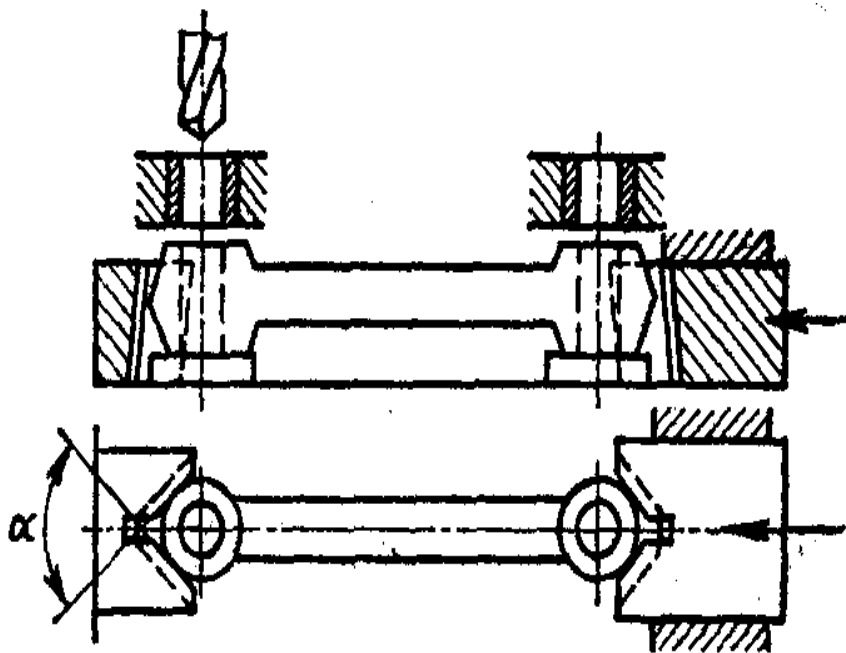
Схема приспособления для одновременного сверления отверстий рычага
